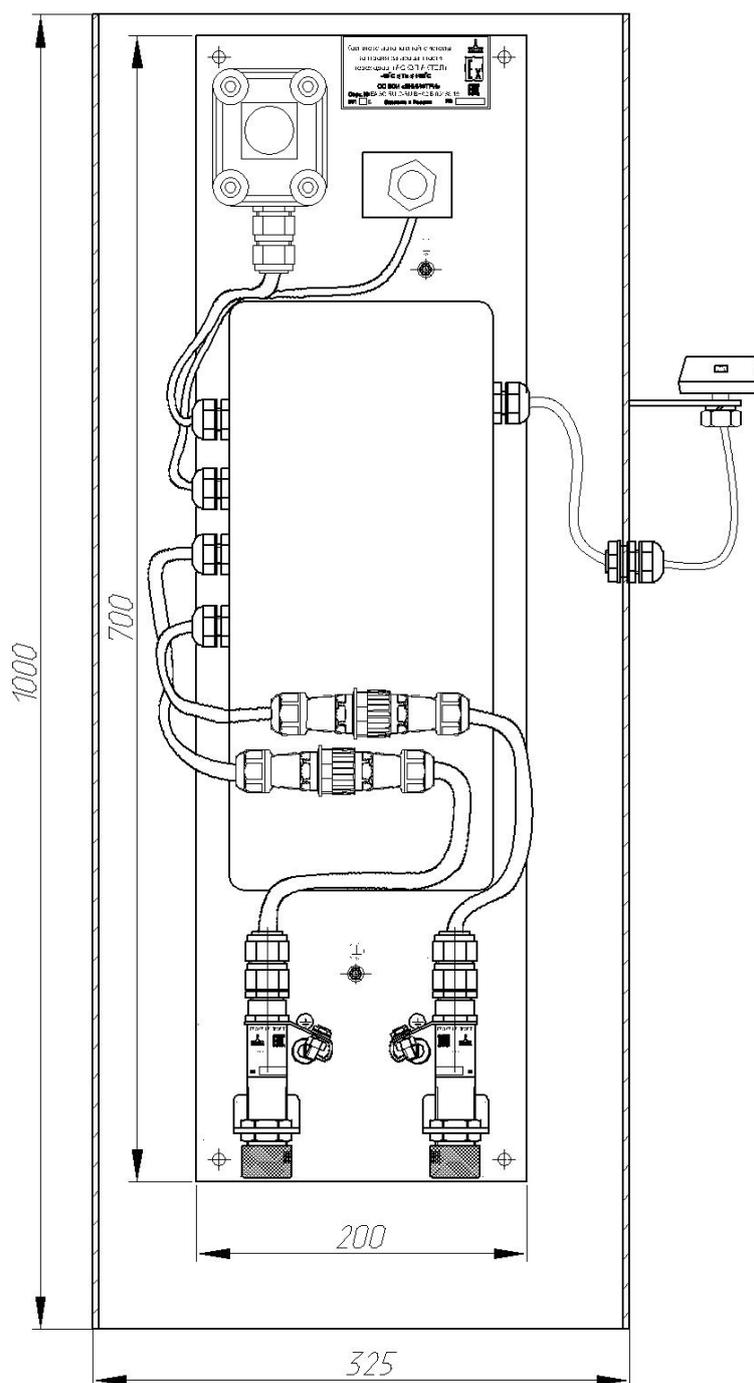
Внешний вид и габаритные размеры комплекса «АСКЗП-АКТЕЛ» исполнение 3 для размещения в корпусе вариант 1
